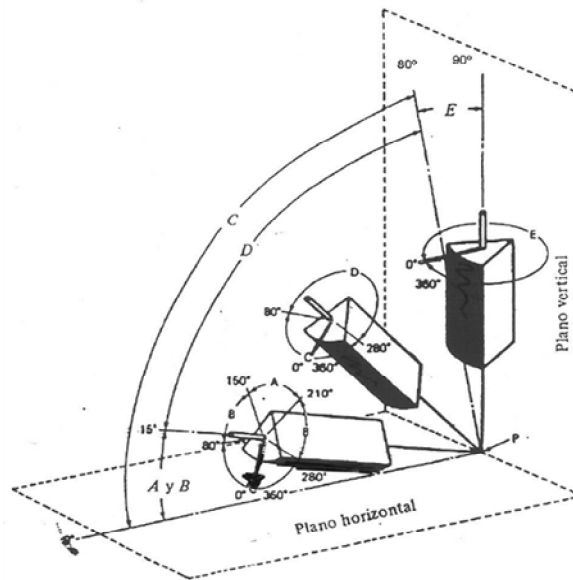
Posiciones del soldador para las distintas posiciones de realización de la soldadura [28].
